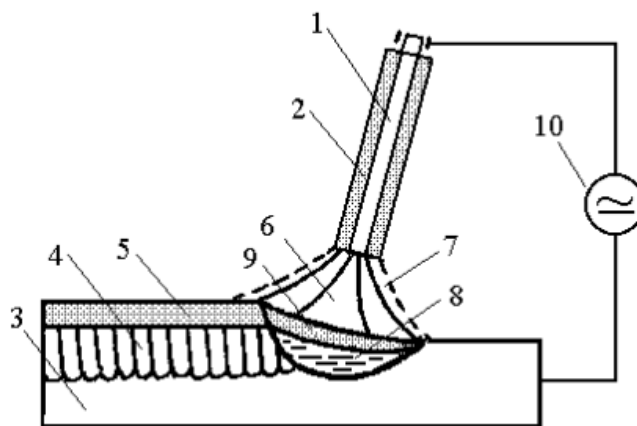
Схема ручного дугового зварювання покритим електродом
